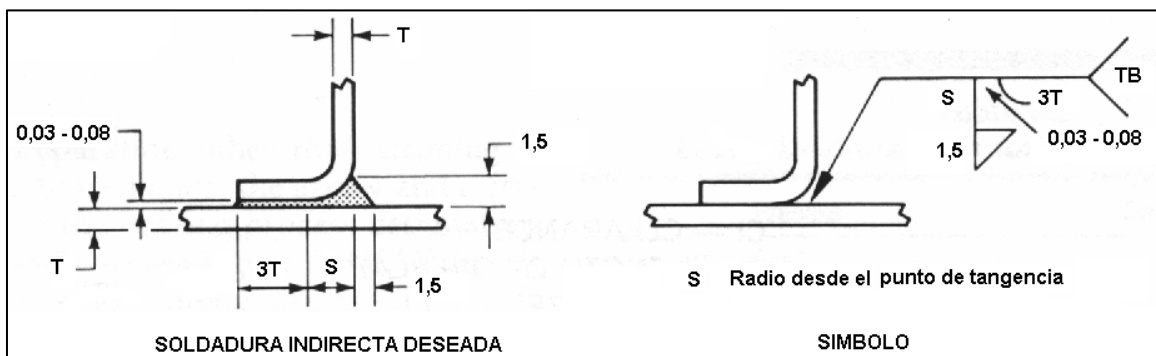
Aplicación de símbolos de soldadura indirecta, ranura – bisel – campana y filete.
